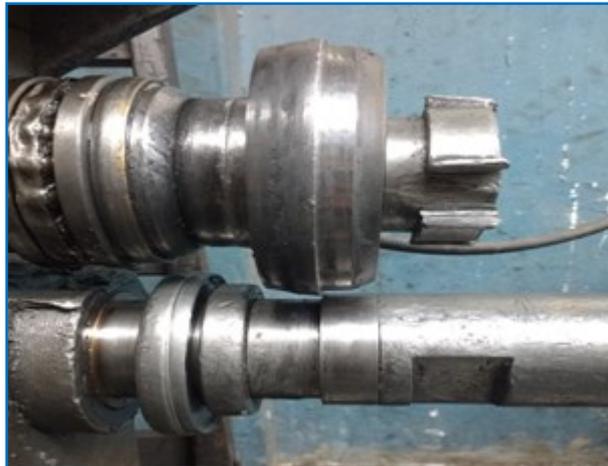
Detalle de los cilindros giratorios de la máquina cortadora de chapa. El cilindro superior es el que posee la cuchilla, mientras que en el inferior se coloca la pieza. (Imagen suministrada por la empresa)
